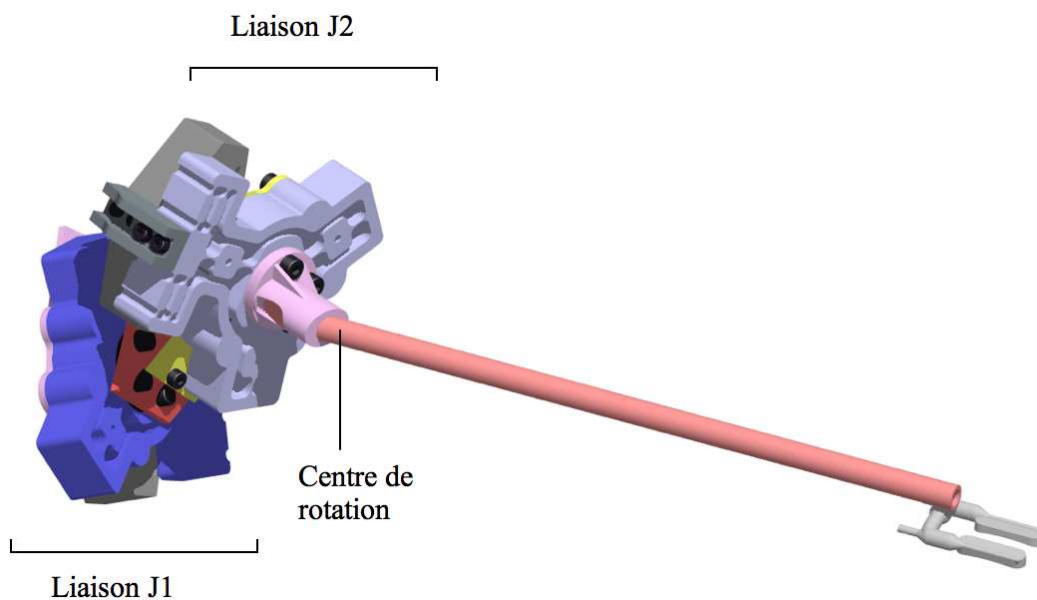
Vue CAO du dispositif Cardiolock 2.
